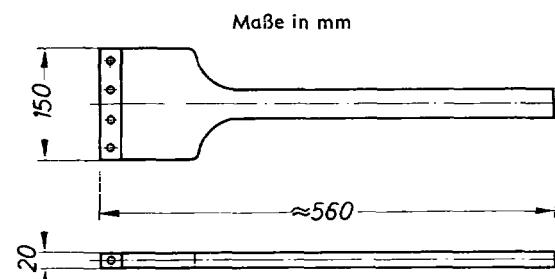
Stampfer für Biegekörper, Gewicht: 0,675 bis 0,720 kg
